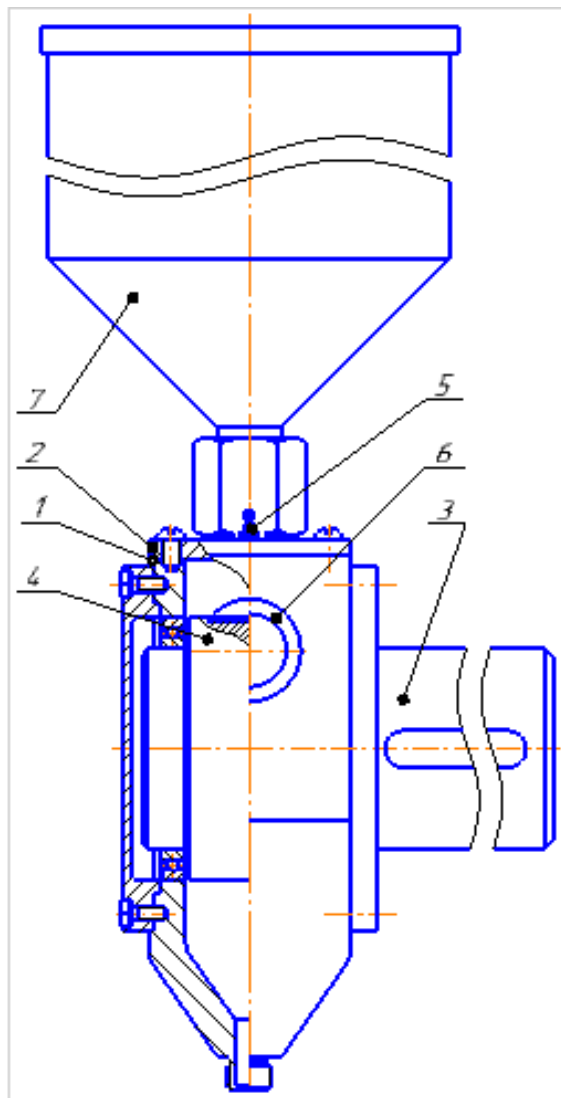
Конструкція порошкового дозатора: 1 – корпус; 2 – кришка; 3 – вал; 4 – барабан із заглибленнями; 5 – штуцер для подачі газу; 6 – оглядовий отвір; 7 – бункер для порошкової суміші
